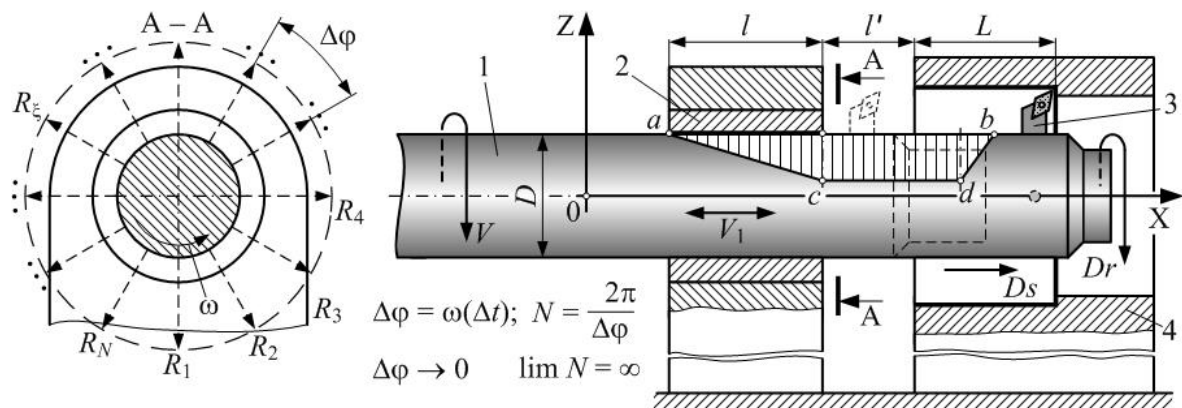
Модель контакта поверхностей вкладыша подшипника скольжения и корпуса борштанги:  $R_i$  – вектор реакции опоры (вкладыша)
